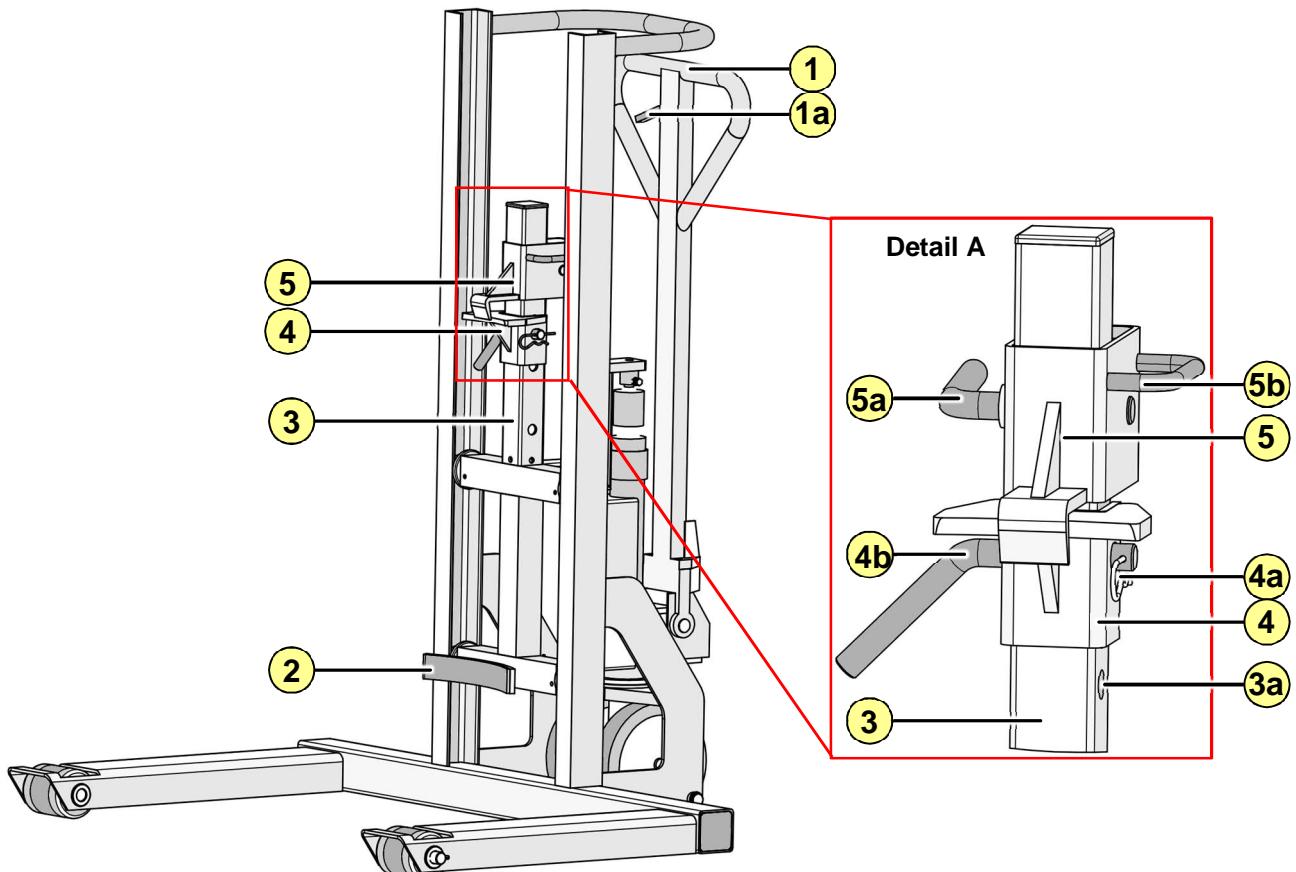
Baugruppen Fassheberoller, Typen FHR 600 G
